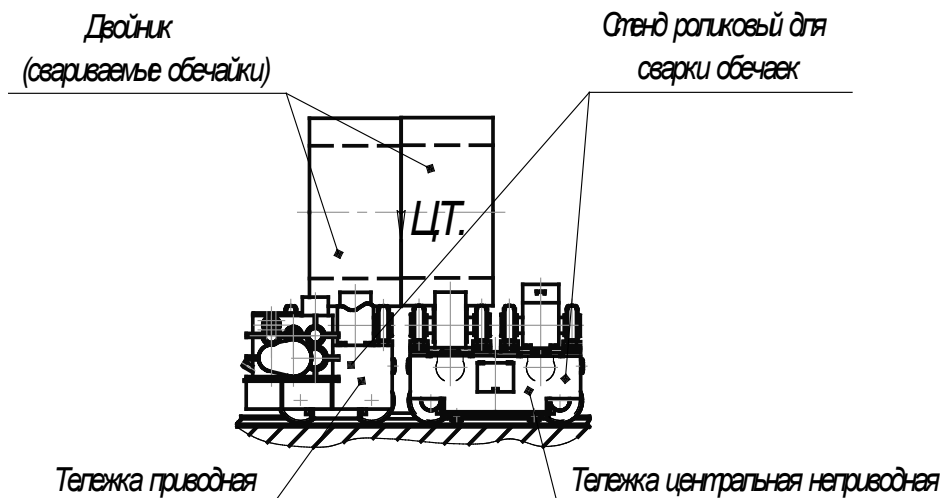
Схема установки рулонированных обечаек на роликовый стенд для сварки
